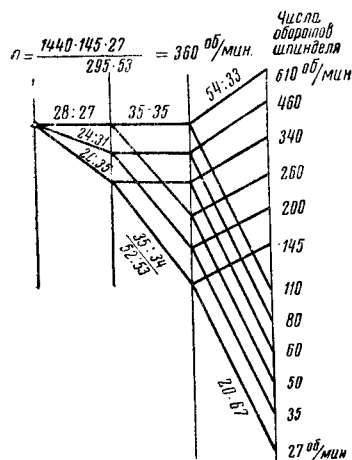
График чисел оборотов шпинделя токарно-револьверного станка 1К36
